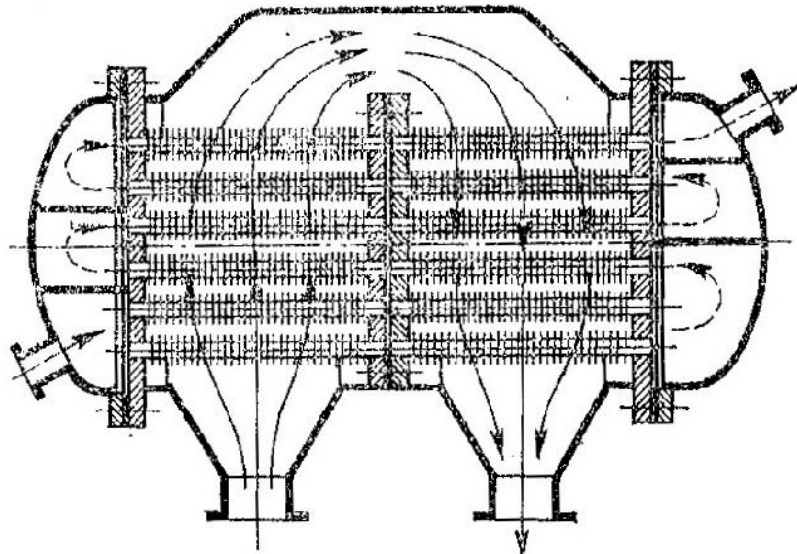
Принцип устройства кожухотрубного газоохладителя.
